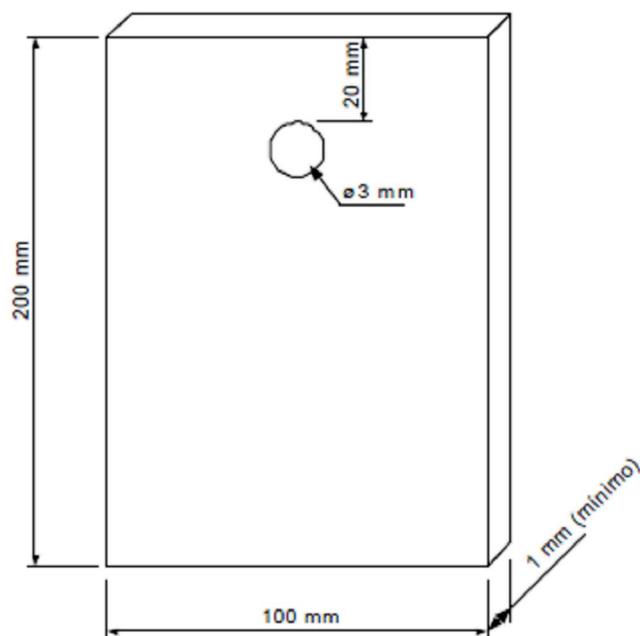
ilustração esquemática do corpo-de-prova para aplicação de tinta (furo central)
